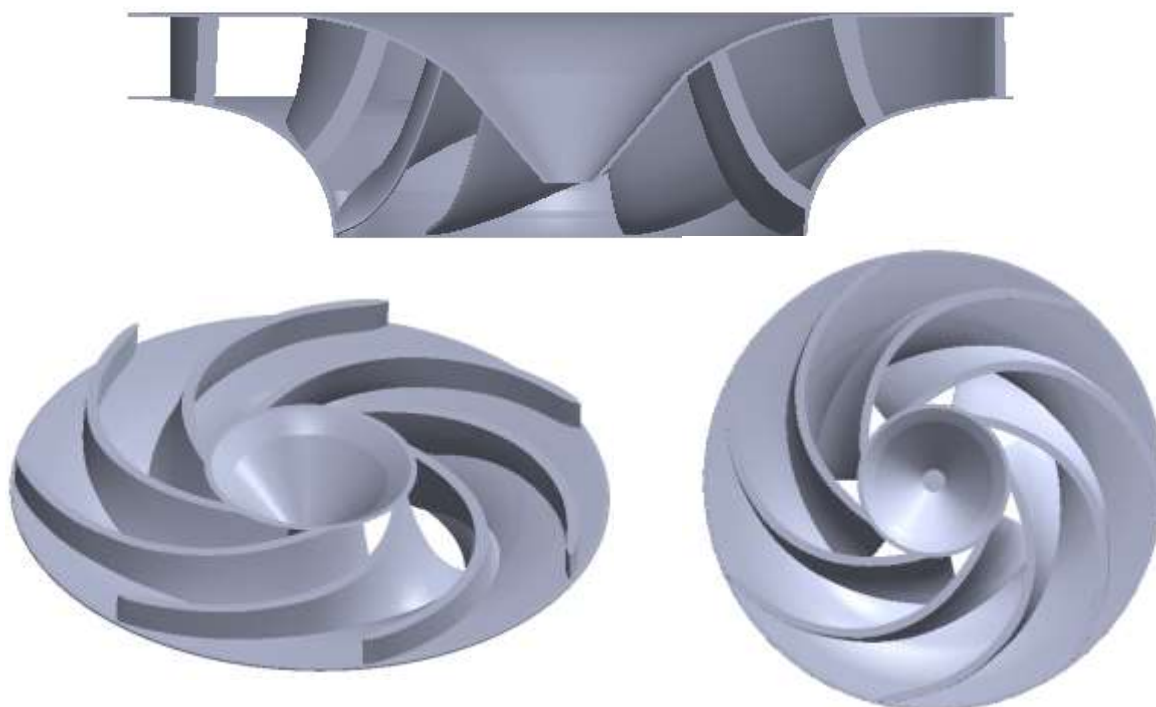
Vista de perfil seccionada y vista isométrica/superior seccionadas.
